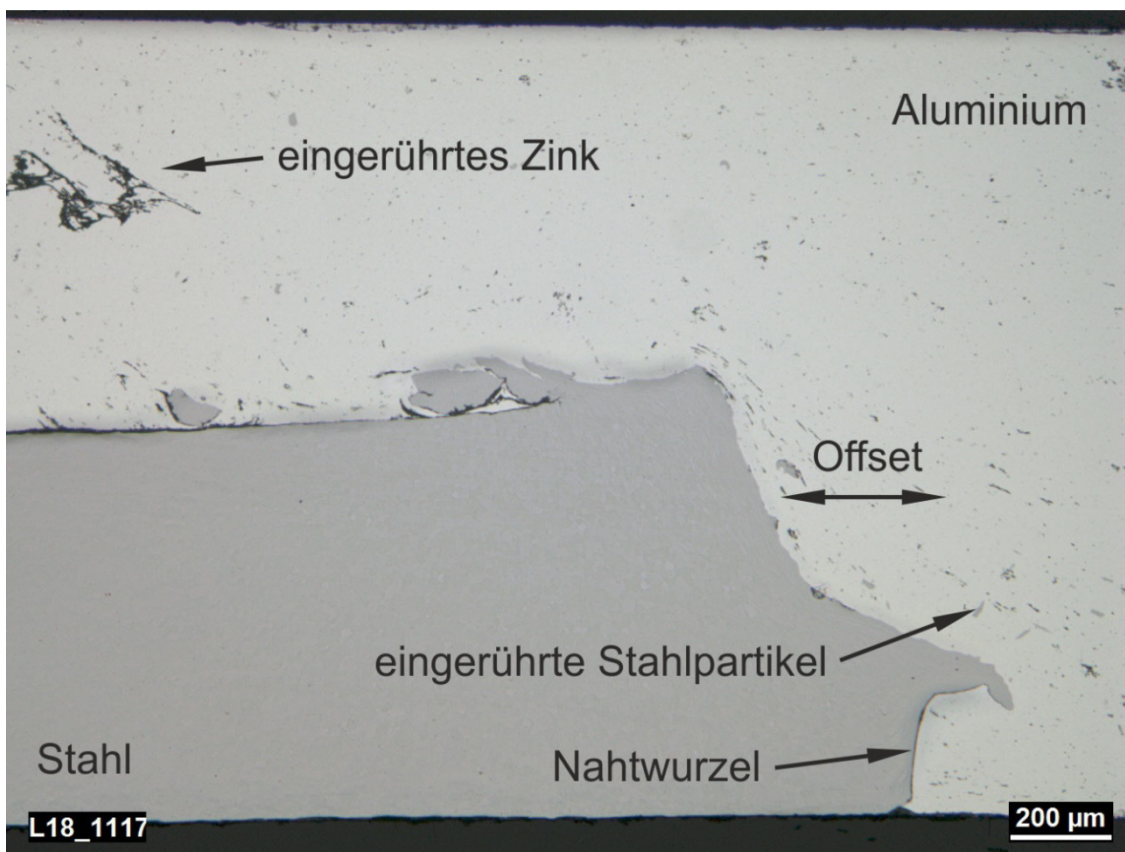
Schliffbild der Schweißnaht PS_2
